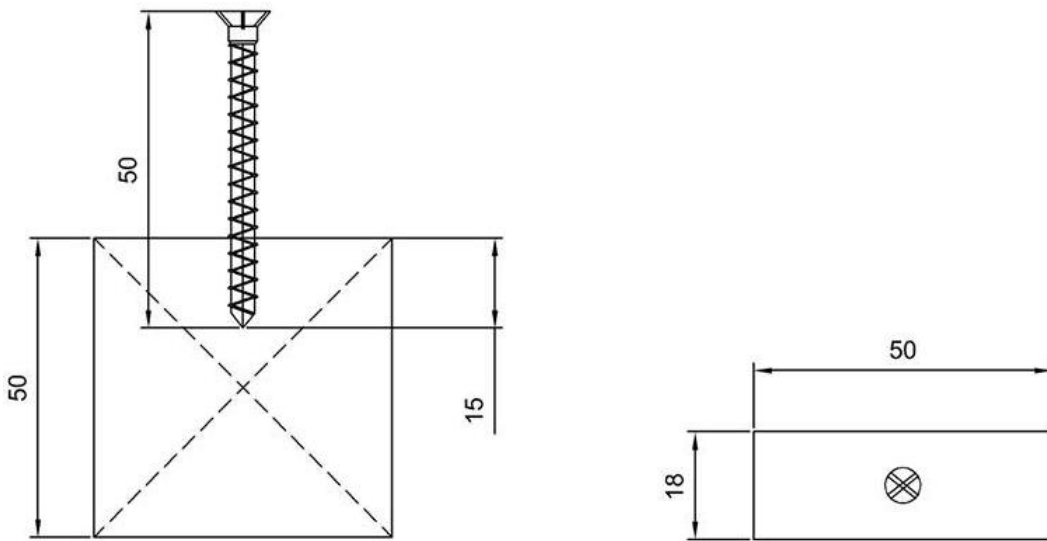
Testlerde kullanılan vida ölçüleri (mm)
